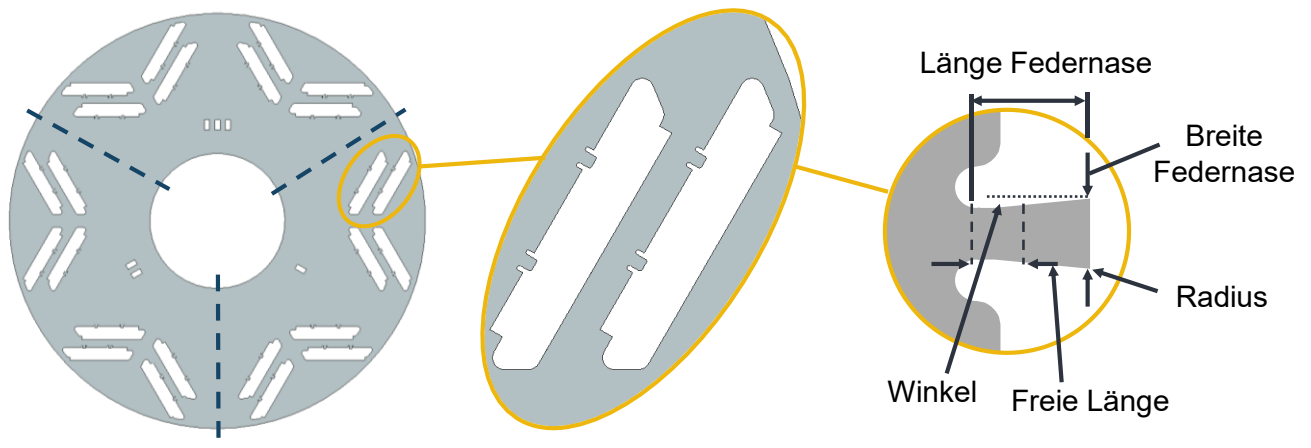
Blechschnittgeometrie für die Magnetfixierung mit Federnase.
